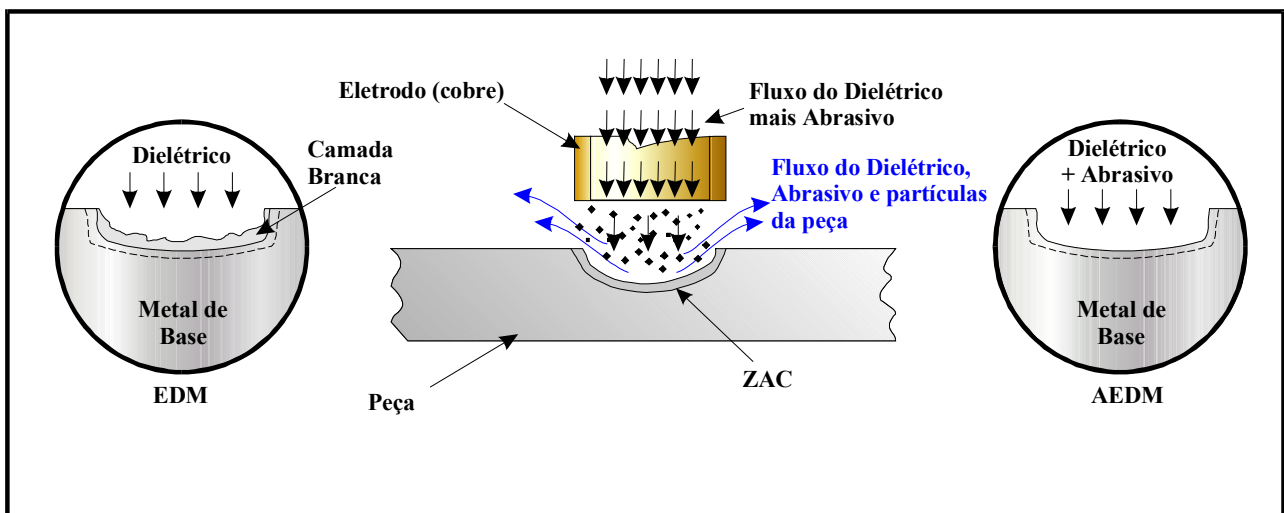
Princípio da Usinagem Híbrida (EDM + AWJM).
